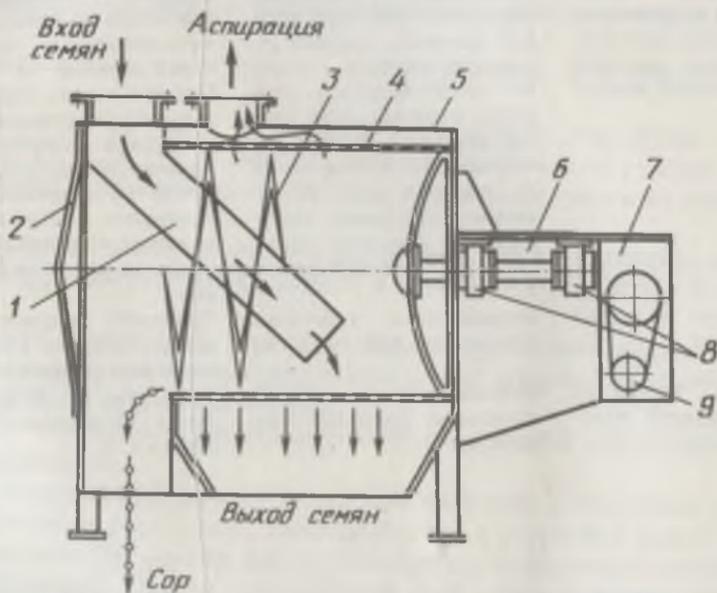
Барабанный сепаратор А1-Б30 (скальператор)
